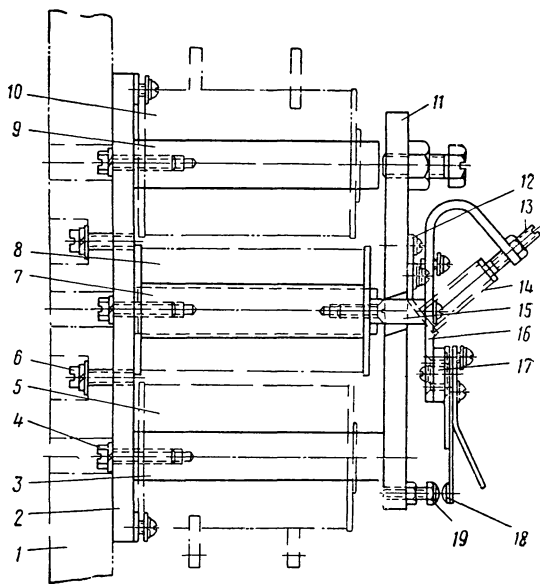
Реле обратного тока типа Р-44А-О: 1—доска; 2—основание; 3, 7 и 9—сердечники; 4 и 6—винты; 5—дифференциальная катушка; 8—серийная катушка; 10—шунтовая катушка; 11—якорь; 12—планка; 13—регулирующий винт; 14—пружина; 15—держатель якоря; 16—скоба; 17—пружина; 18—неподвижный контакт; 19—подвижной контакт
